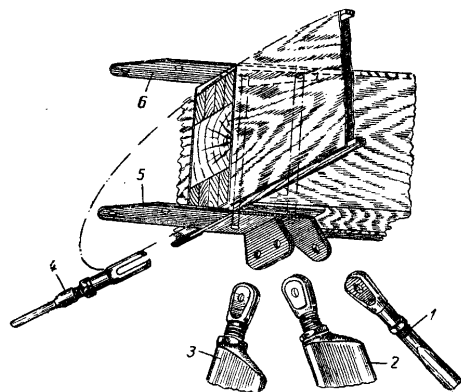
Передний узел крепления верхнего крыла и кабана центроплана (левый).
